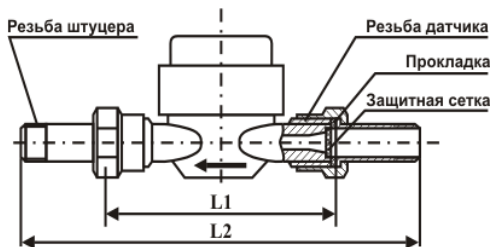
Габаритные и присоединительные размеры Датчиков ДР18, ДР19
